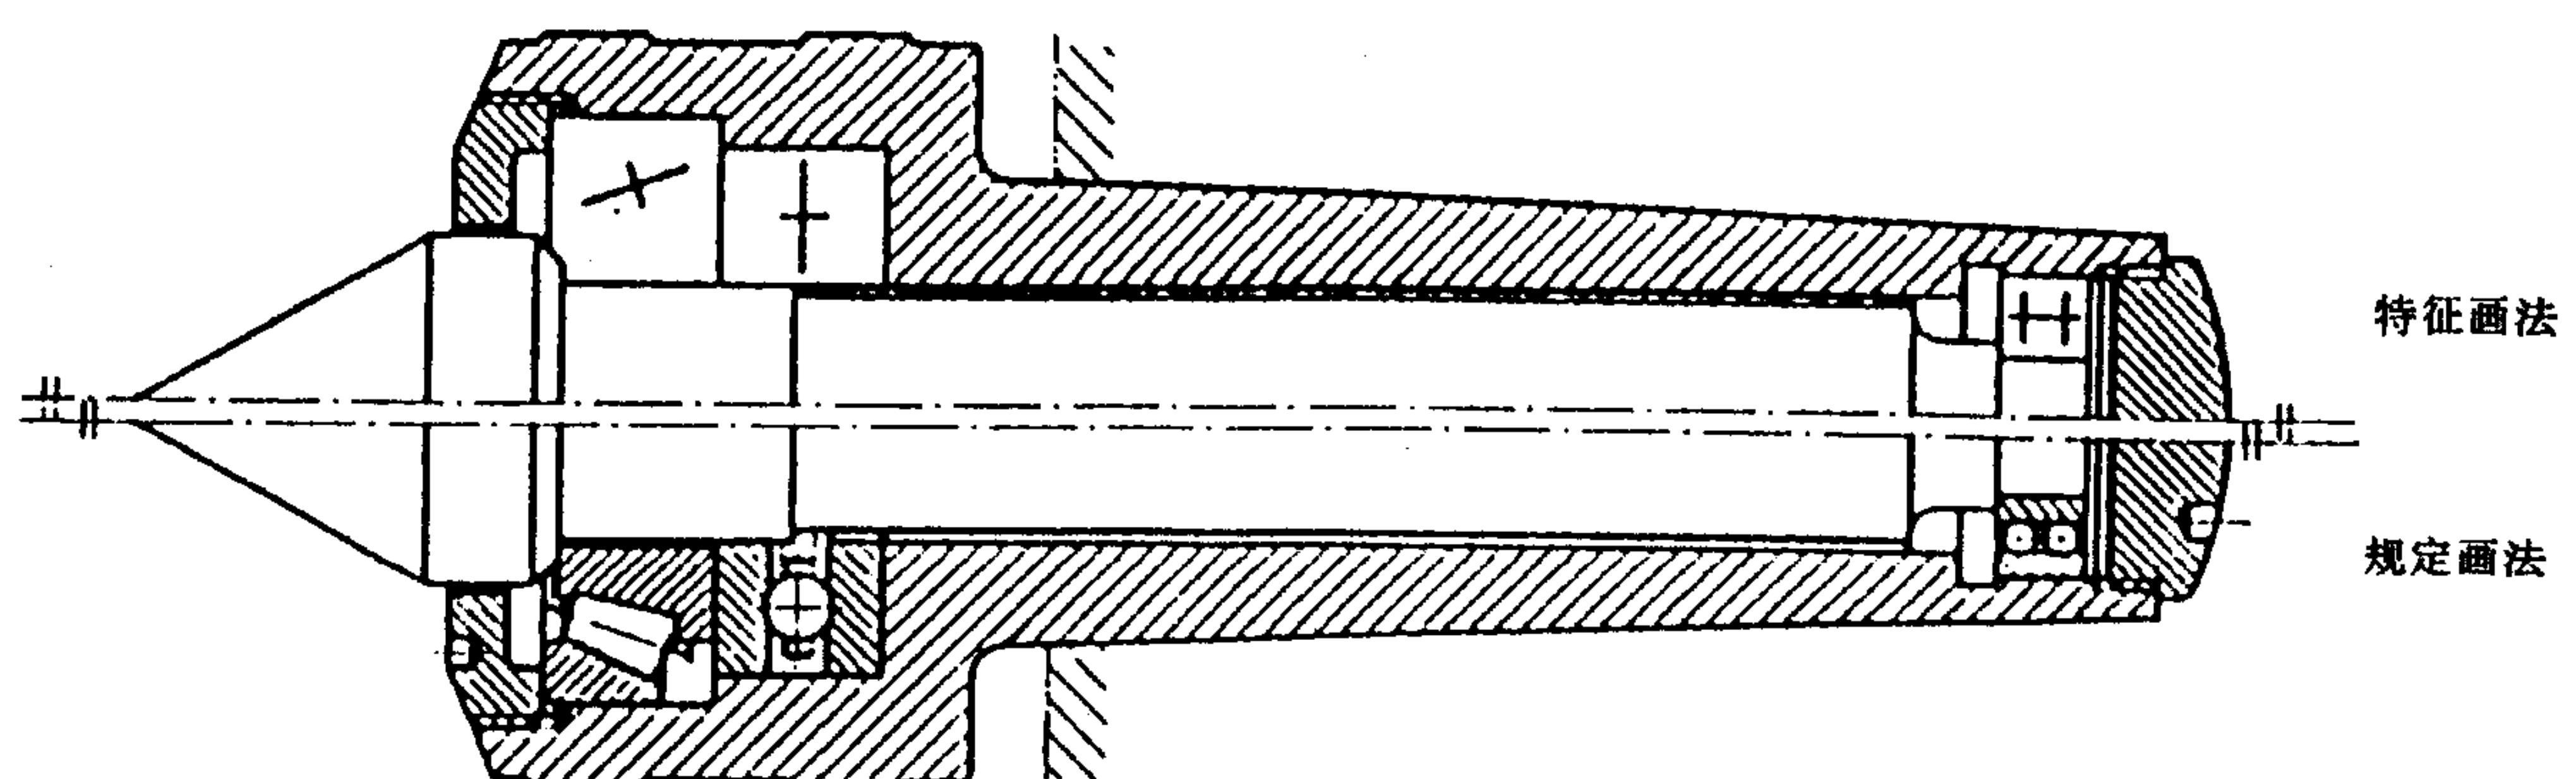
圆锥滚子轴承、推力球轴承和双列深沟球轴承在装配图中的画法
